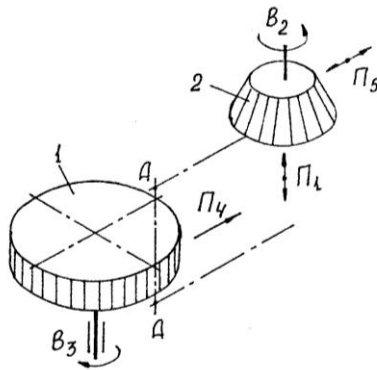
Схема способа долбления прямозубых цилиндрических колес
